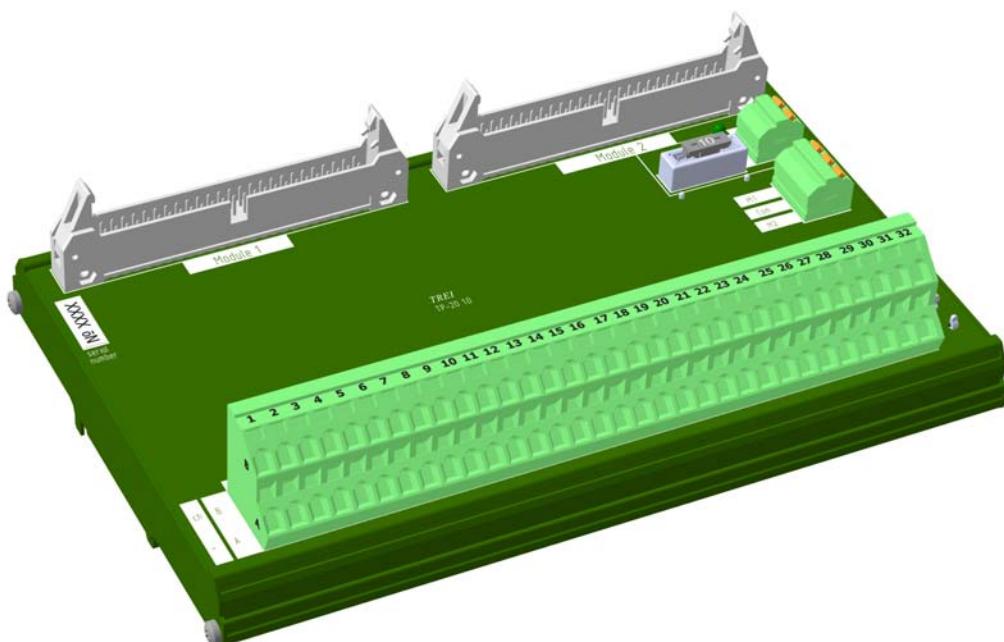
Чертеж общего вида ТР-2FD с указанием габаритных размеров
